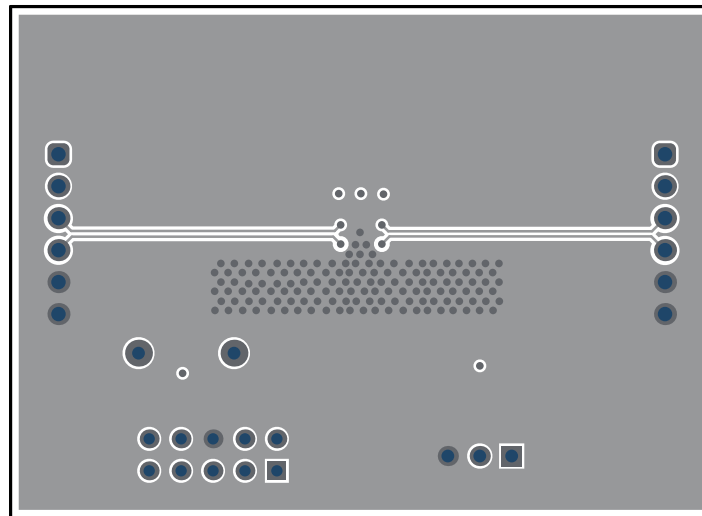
TPSM83102EVM-125 PCB - 底层 (顶视图)
